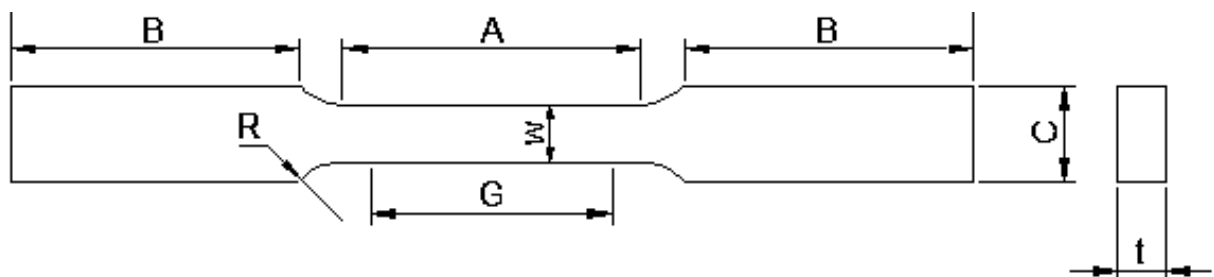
Forma y dimensiones utilizadas en las probetas a tensión.
